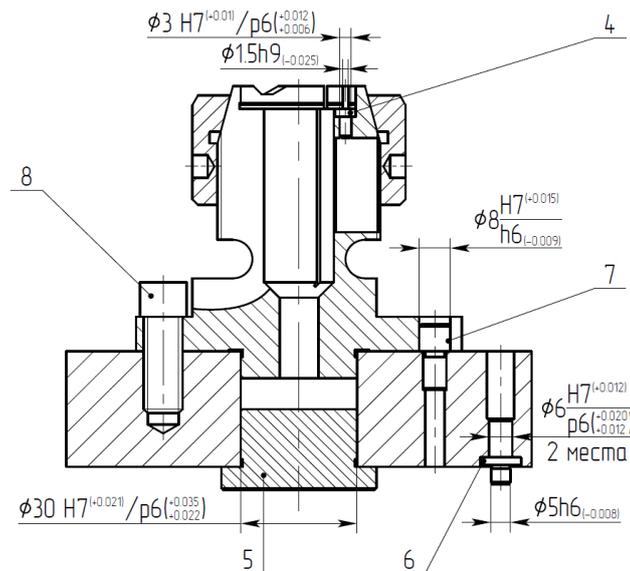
Станочное приспособление - Оправка зажимная для детали «Магнитопровод»
